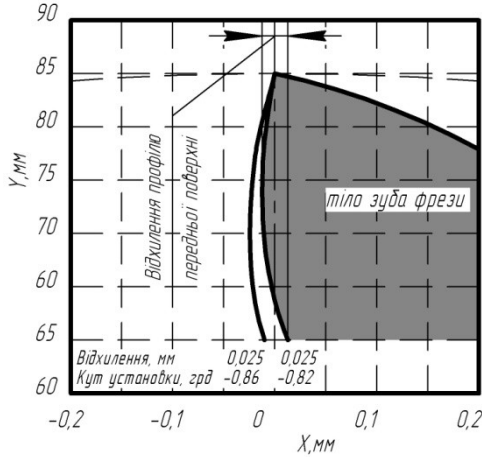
Профіль передньої поверхні фрези у межах допуску:
